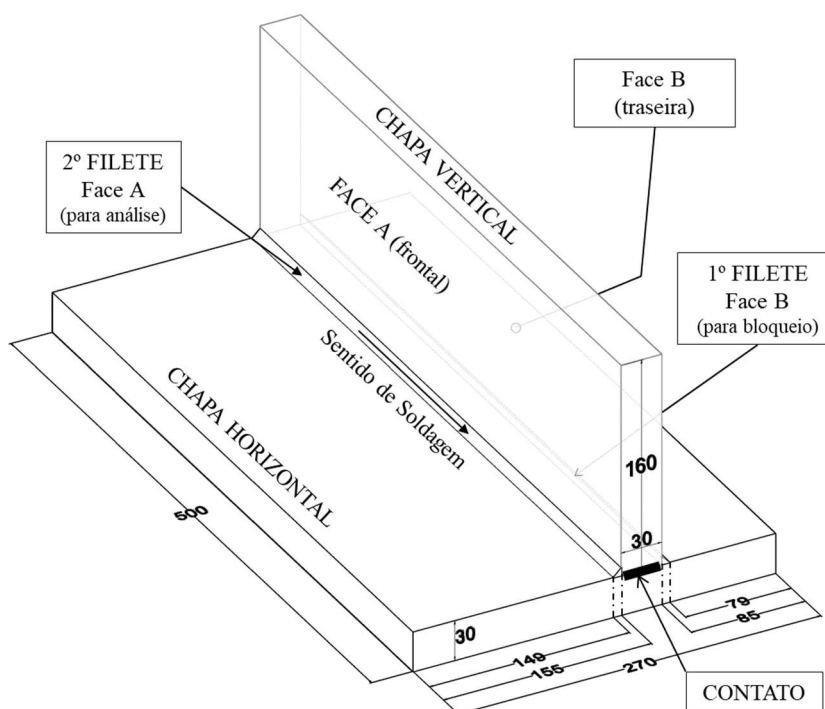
Posicionamento e dimensionamento das chapas para soldagem. A face B, na qual é soldado o primeiro filete (oculto pela chapa vertical) é denominada face traseira. O filete 1 bloqueia a rota de fuga dos gases gerados durante a soldagem do segundo filete, localizado na face A (ou face frontal). Todas as dimensões em mm.
